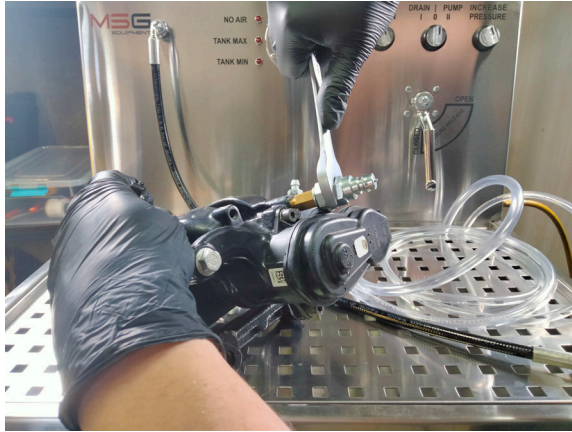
Montaje de la boquilla con el adaptador en la pinza
